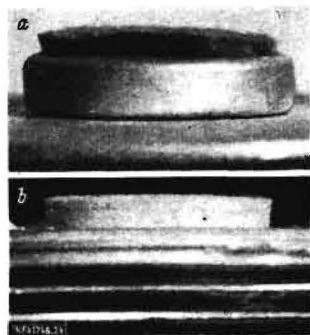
Ausführung der Enddichtung von Filterpaketen *a* schlecht, *b* gut
